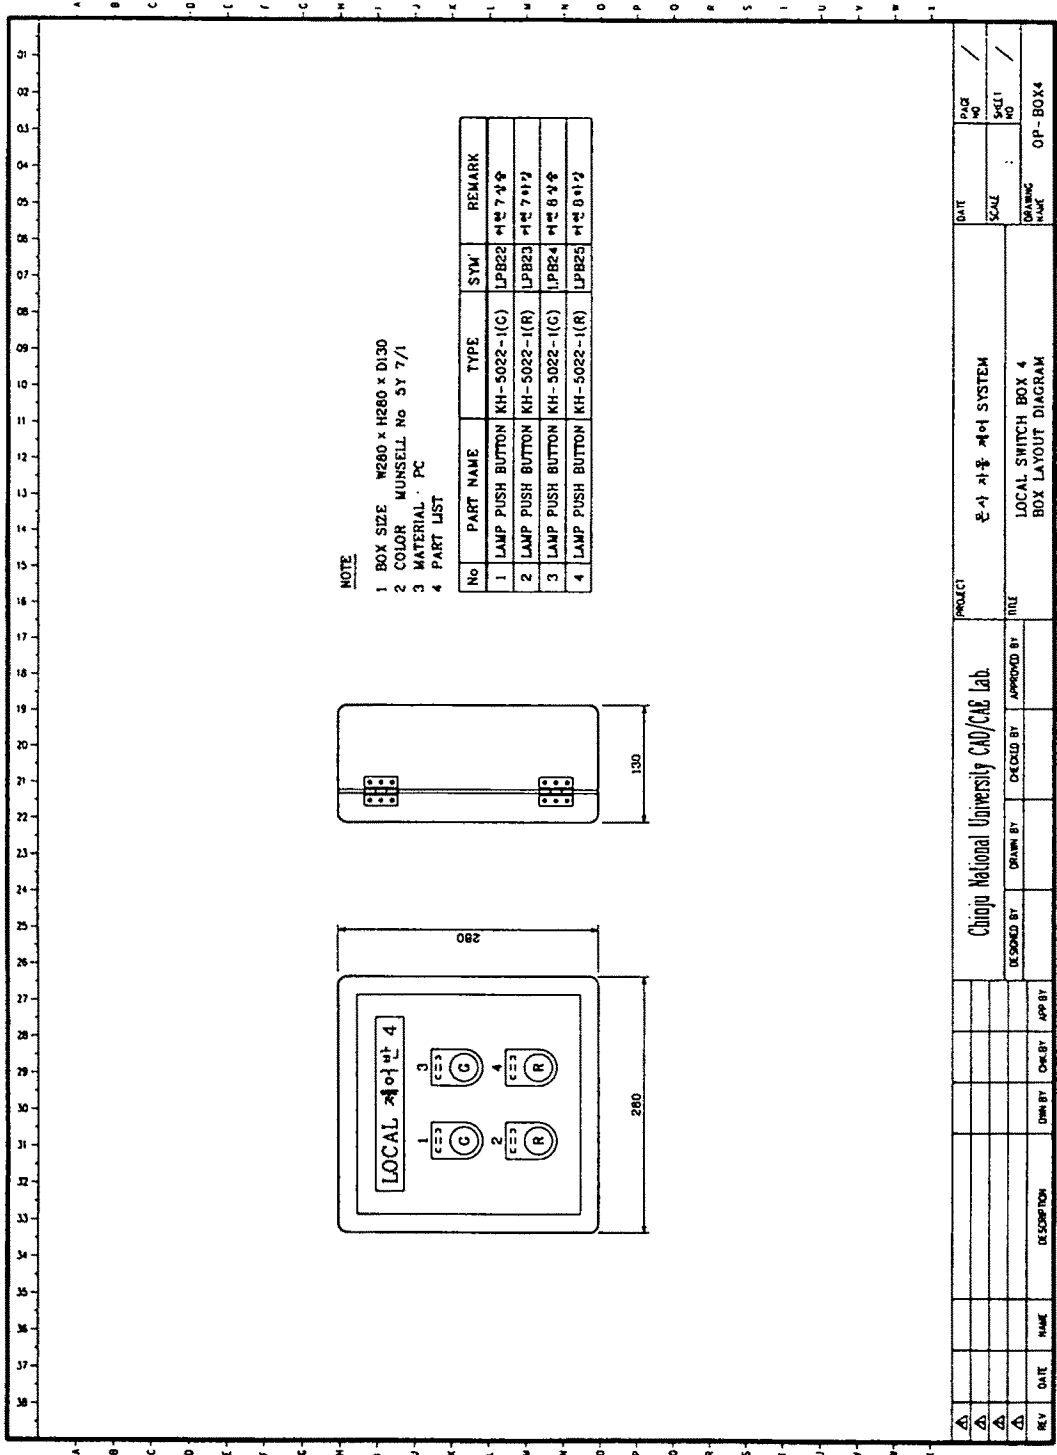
스위치 박스 배치도(Local switch box layout diagram) #4
